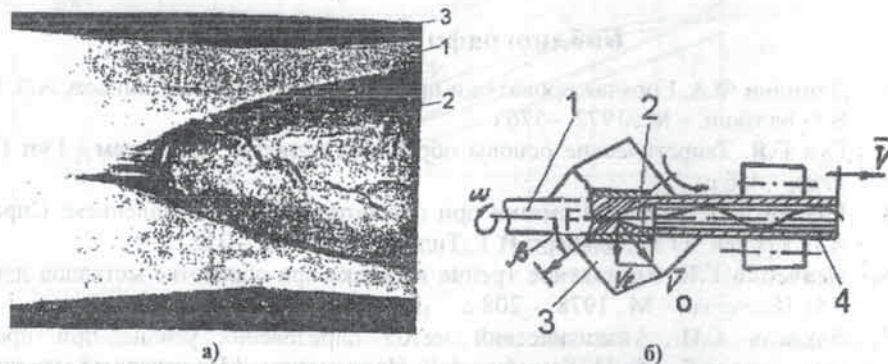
Мгновенный очаг деформации а) и процесс прошивки б) заготовки на прошивном стане ТПА
